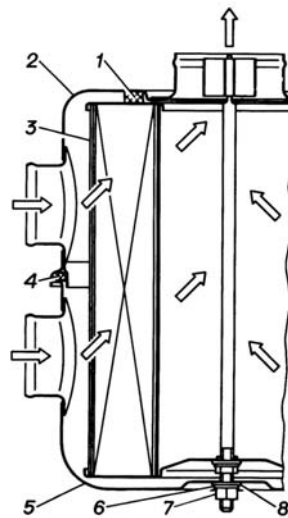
Воздушный фильтр: 1, 4 и 8 – прокладки; 2 – корпус фильтра (верхняя часть); 3 – фильтрующий элемент; 5 – корпус фильтра (нижняя часть); 6 – шайба; 7 – гайка
